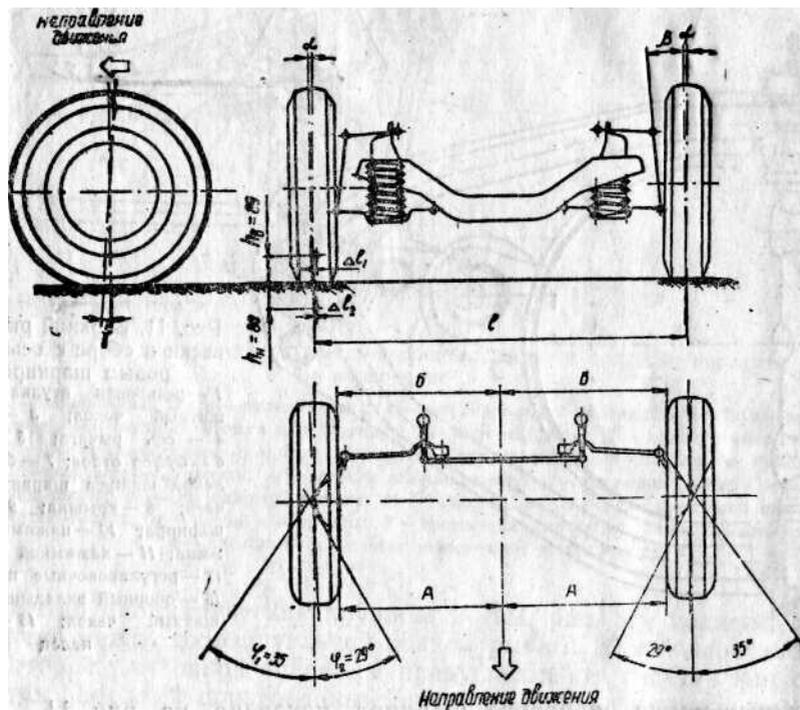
Кинематическая схема подвески передних колес и рулевого привода
